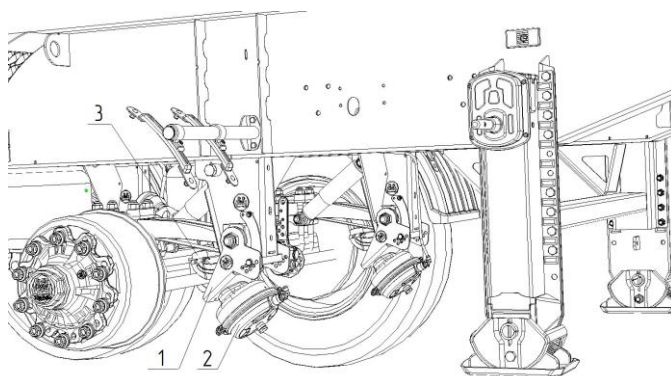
А. Двухсторонний механизм подъёма оси с пневмцилиндром.
